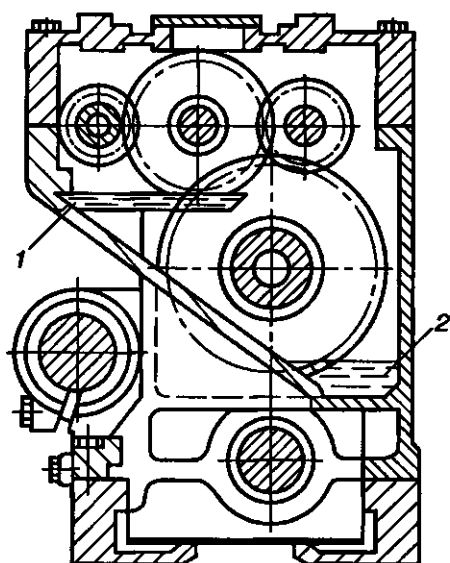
Смазка в масляной ванне с применением дополнительного резервуара: 1 – масляная ванна; 2 – дополнительный резервуар
